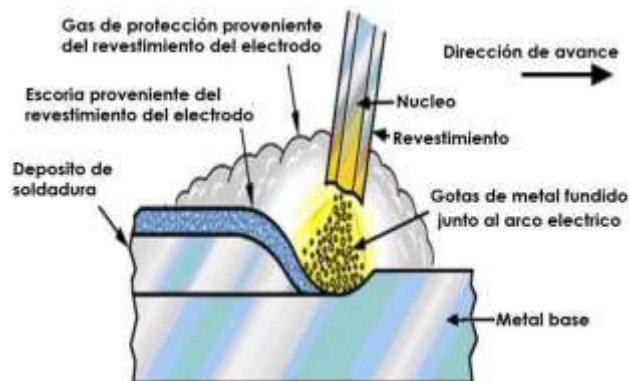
Soldadura con por arco eléctrico y electrodo revestido (SMAW).
